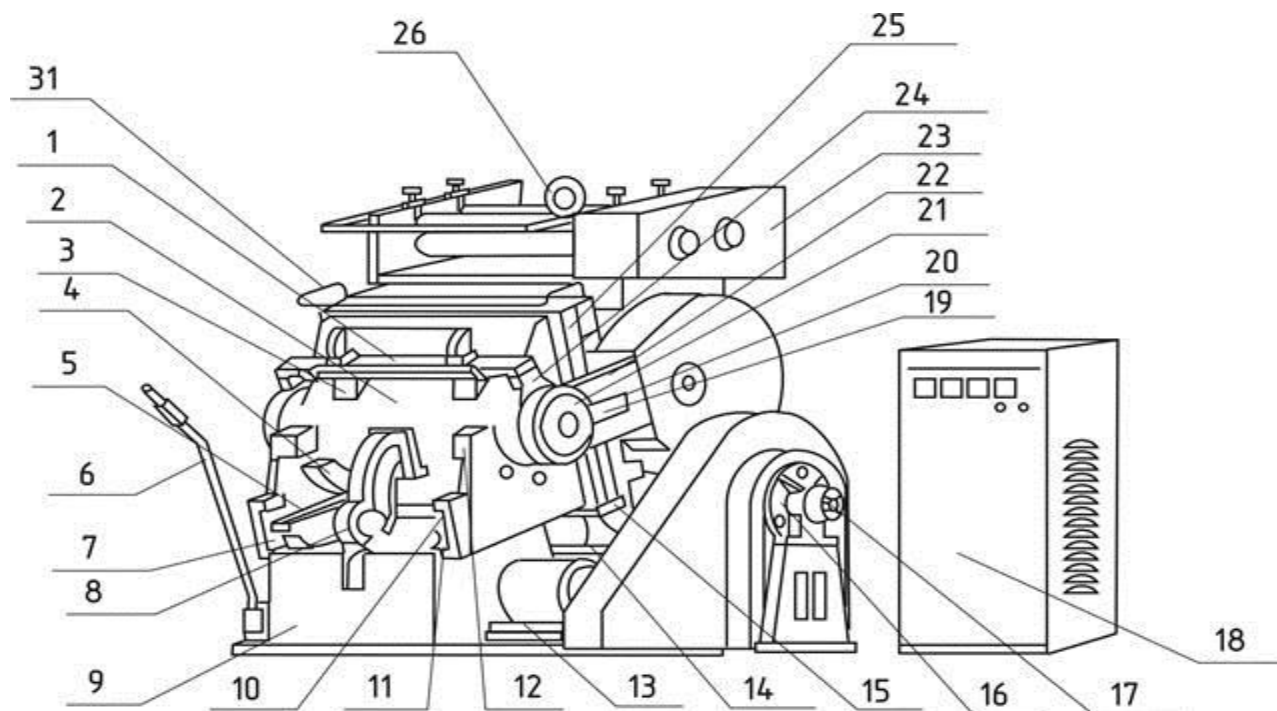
Чертеж основных узлов позолотного штанцевального прессы
